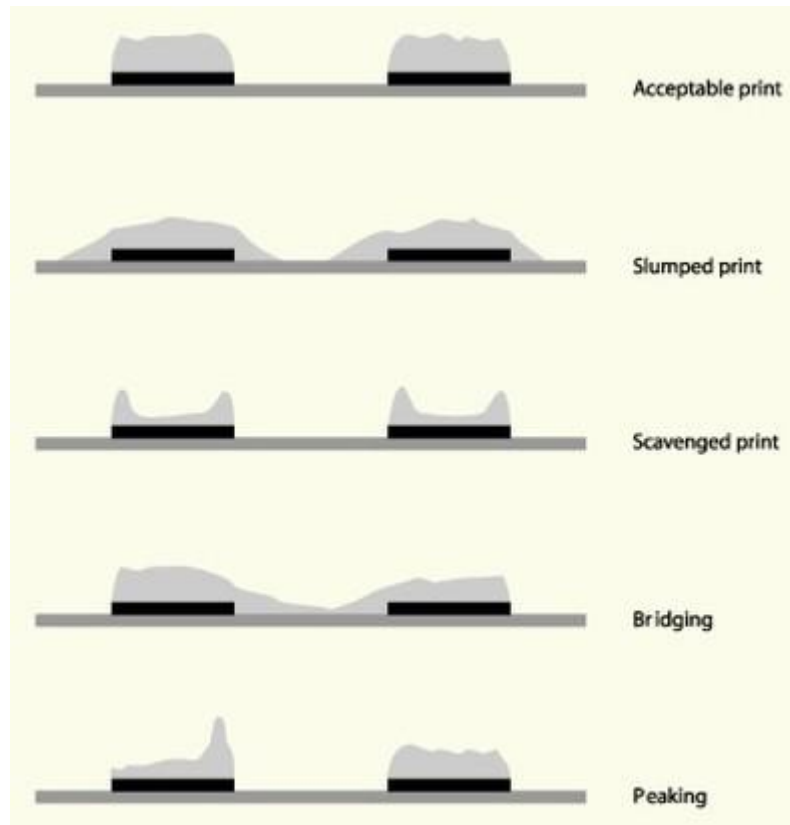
Resultados possíveis na inspeção de impressão da pasta de solda.
